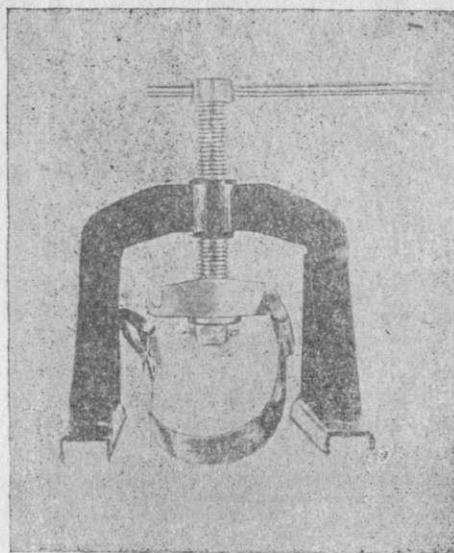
Приспособление для вынимания коленчатого вала из картера
